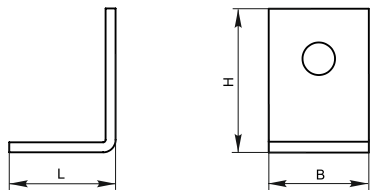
Уголок крепёжный одинарный для STRUT-профиля
